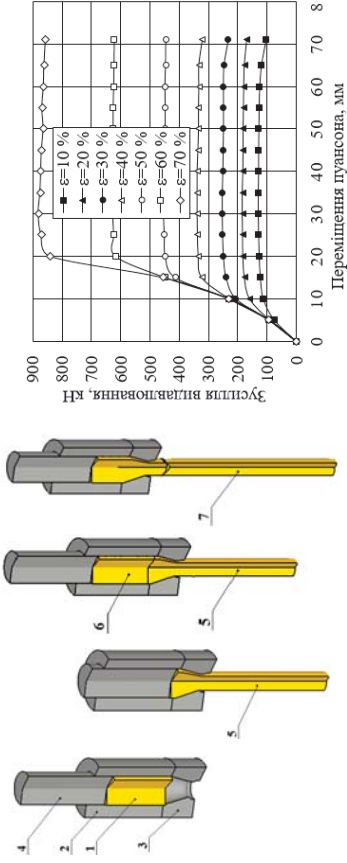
Розрахункові схеми в розрізі на початку та в кінці видавлювання першої та другої заготовки
